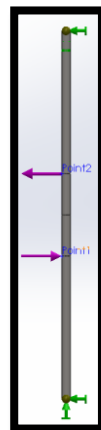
Fuerzas aplicadas al eje del sistema de ejes vertical.
